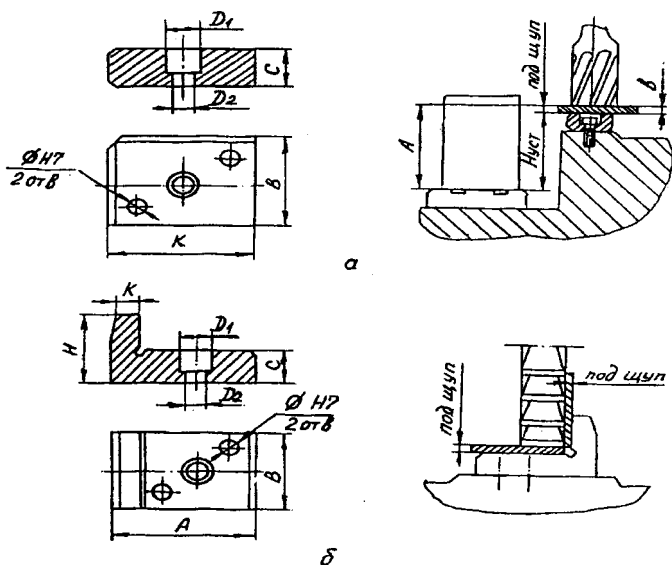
Схема настройки и стандартные установки для фрез:
